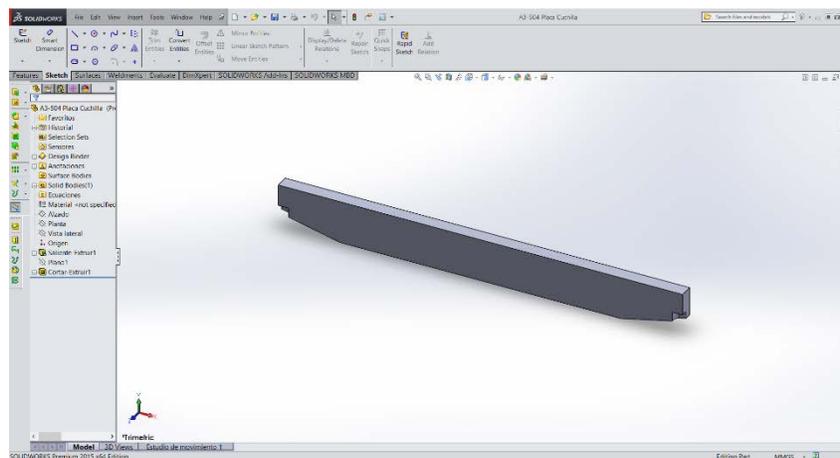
Sólido 3D del plano A3-504 Placa cizalla.
